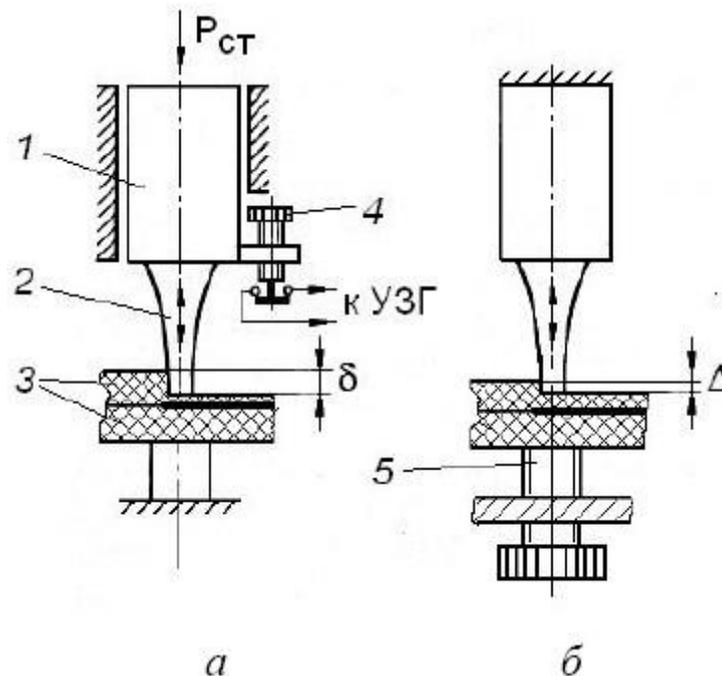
Сварка по схеме с фиксированной осадкой (а) и фиксированным зазором (б): 1 – преобразователь; 2 – волновод; 3 – свариваемый материал; 4 – нажимной штифт для отключения ультразвука; 5 – регулировочный винт-опора
